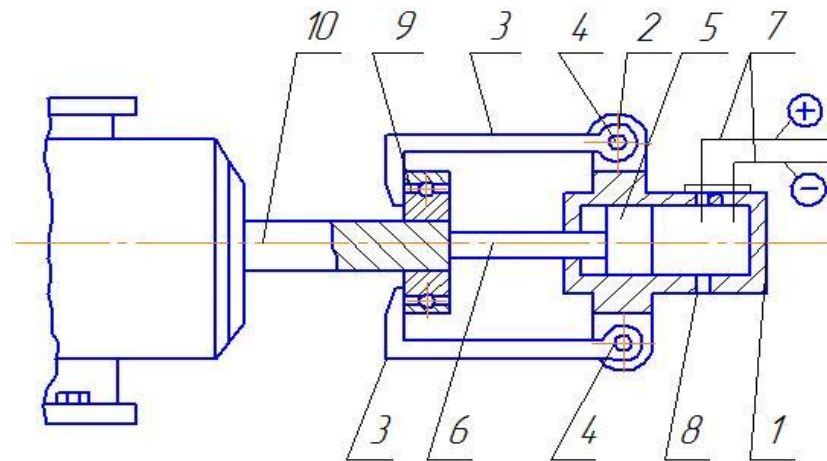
Пристрій для демонтажу підшипників з валів: 1 – корпус; 2 – вушка; 3 – захоплювачі; 4 – фіксуючі болти; 5 – поршень; 6 – силовий шток; 7 – електроди; 8 – штуцер; 9 – деталь, що знімається; 10 – вал.
